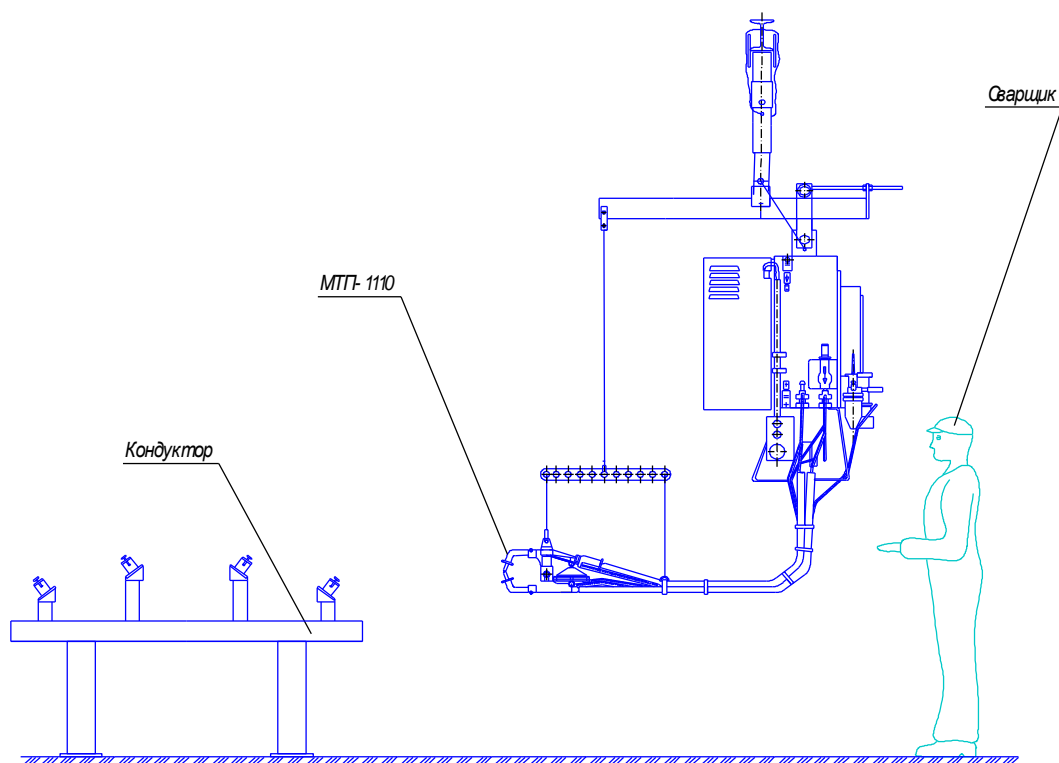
Базовая технология сборки-сварки панели кабины
